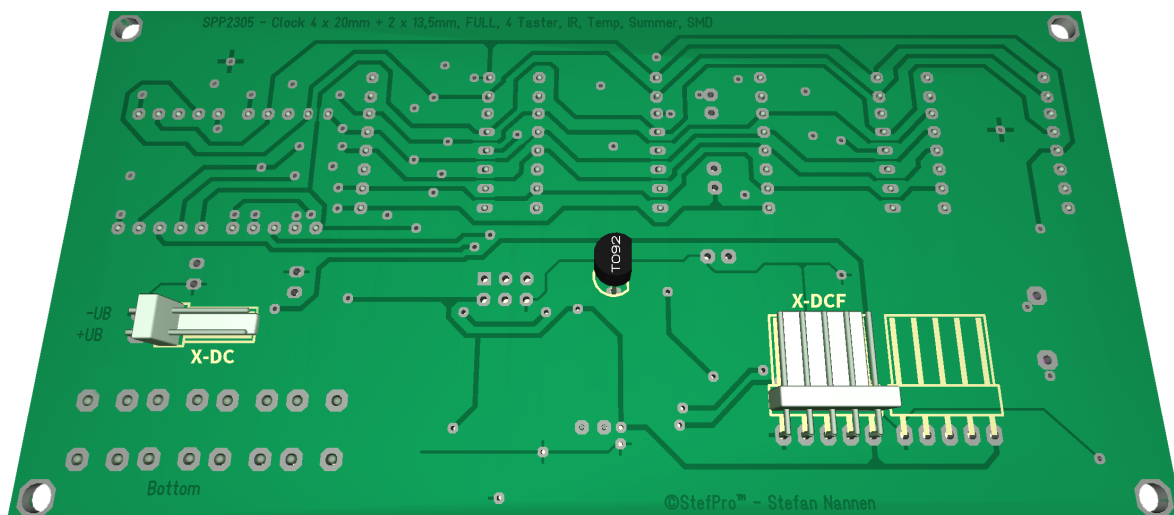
Stecker Beschreibung zum Modul SPH2305.1
